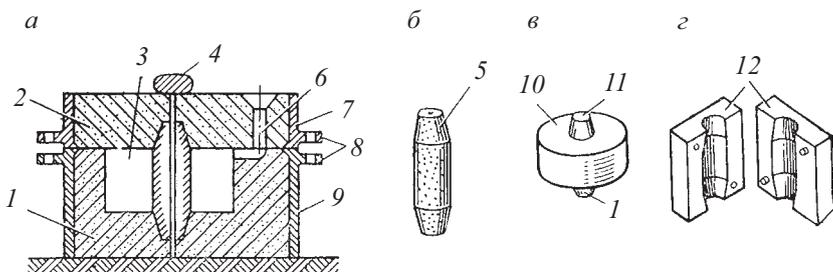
Литейная форма (а), стержень (б), модель (в), стержневой ящик (з) для получения отливки зубчатого колеса
